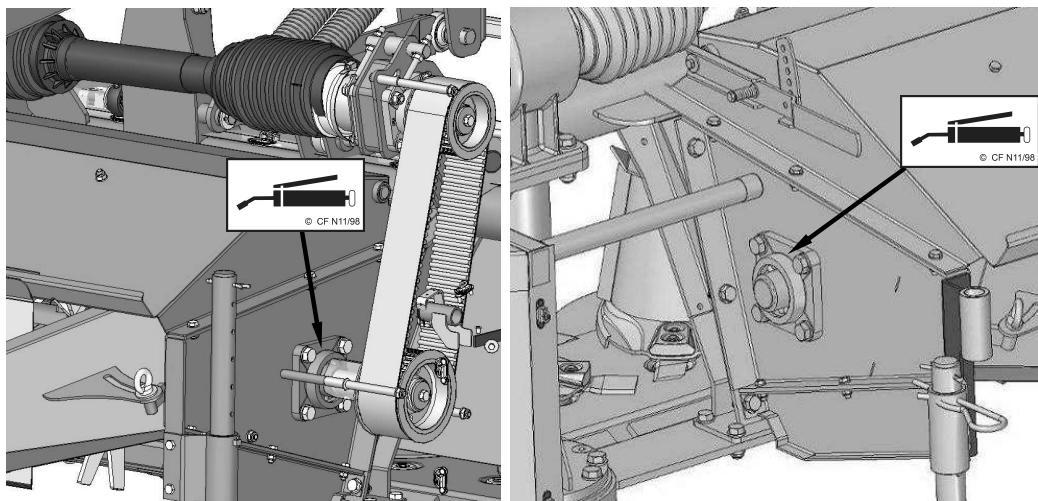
Точка смазки самоустанавливающегося подшипника LT 43
